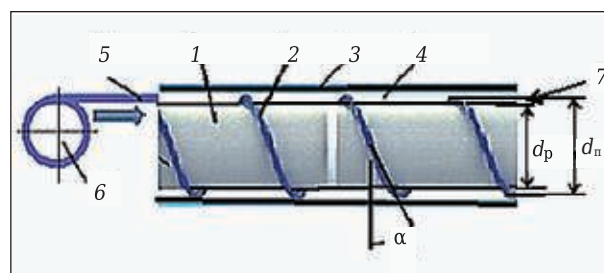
Устройство теплозащиты стенки высокотемпературного цилиндрического аппарата: 1 — стенка; 2 — винтовая труба; 3 — кожух; 4 — зазор винтообразный; 5 — патрубок; 6 — источник сжатого агента; 7 — зазор между наружной поверхностью винтовой трубы 2 и кожухом 3; α — угол подъема винтовой трубы 2; d_n — диаметр винтовой трубы; d_p — диаметр цилиндрического аппарата
